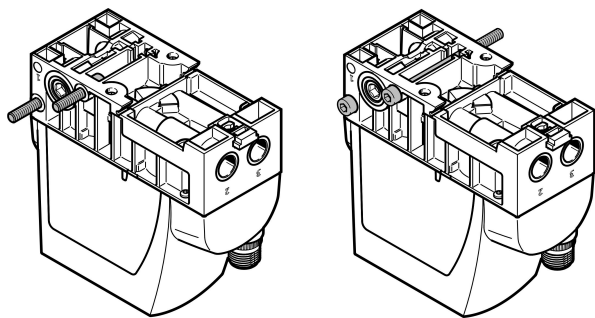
Befestigung über Seitenfläche mit innenliegenden Schrauben M4/
